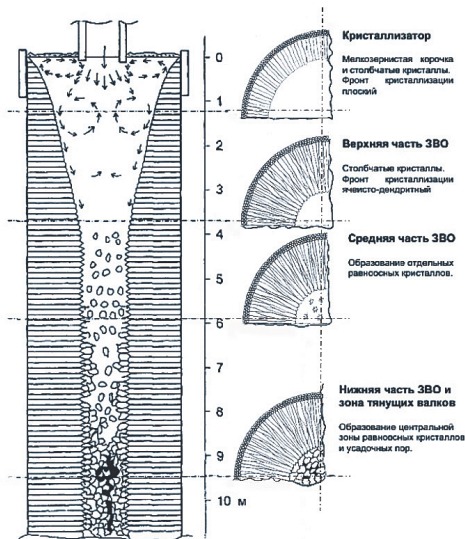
Схема кристаллизации непрерывнолитой заготовки по технологической оси МНЛЗ [2]
